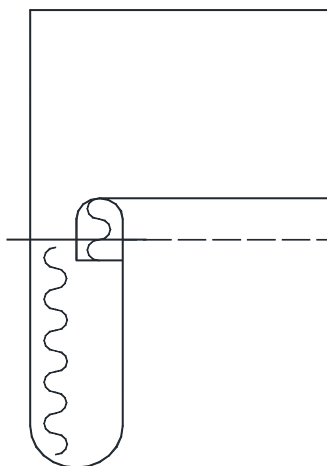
Монтажная схема конструкции низа изделия швом вподгибку с закрытым срезом
